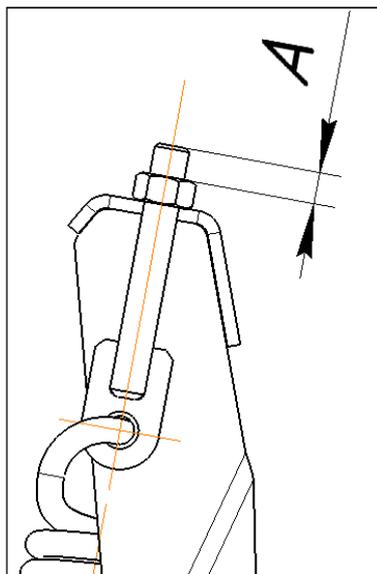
Размер «А» выхода резьбовой части натяжителя без предварительного натяжения пружин подвески
